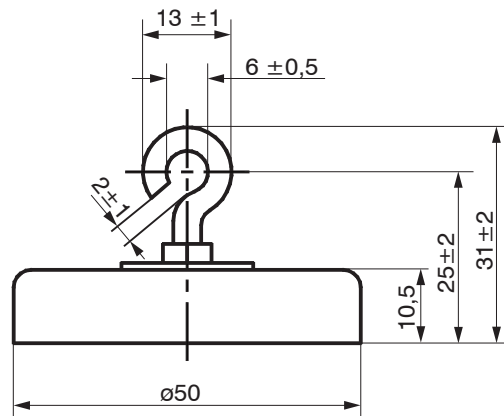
Magnethalter MH1 - WDS, Abmessungen in mm
